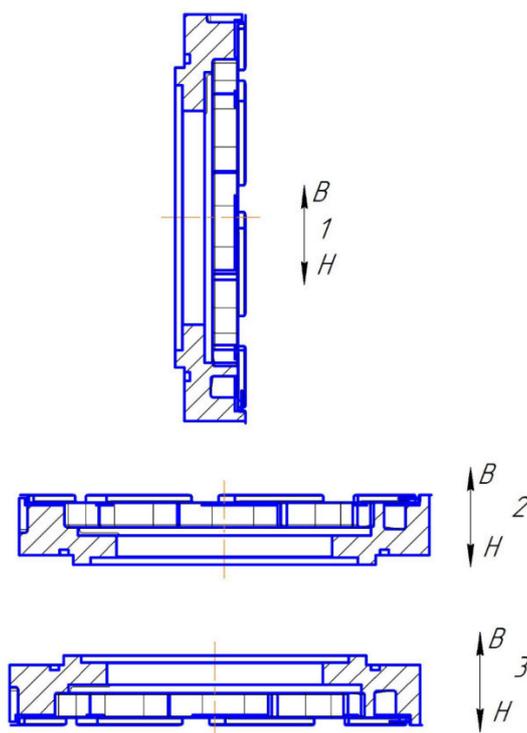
Варианты расположения отливки в форме в период заливки и затвердевания
